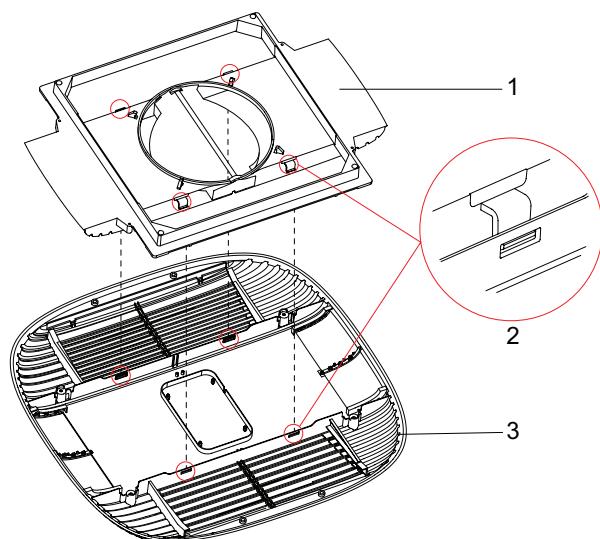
Conexión del conjunto de distribuidor de aire al soporte de montaje
